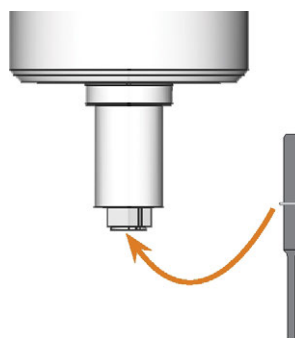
INSÉRER L'OUTIL DANS LA PINCE DE SERRAGE
